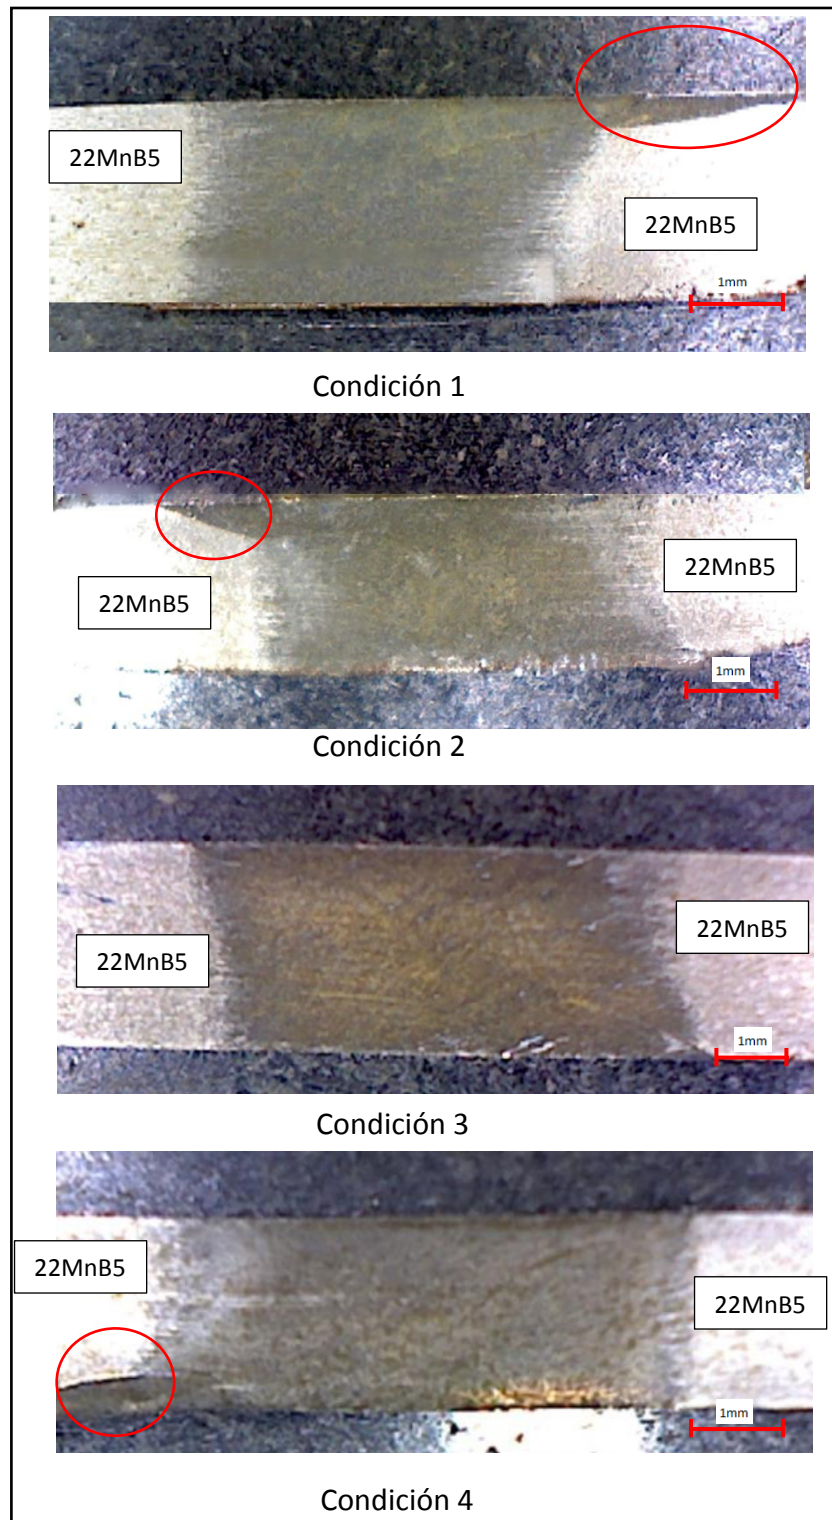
3. Sección transversal del cordón de soldadura para cada condición entre 22MnB5-22MnB5.
